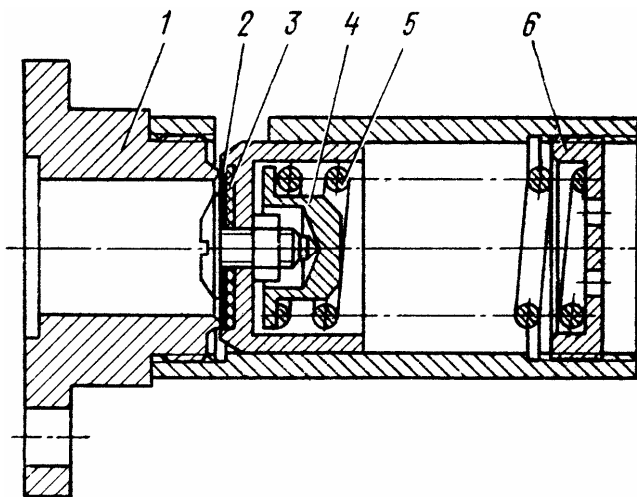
Запобіжний клапан: 1 – сідло; 2 – гумова прокладка; 3 – фторопластова прокладка; 4 – клапан; 5 – пружина; 6 – регулююча гайка
